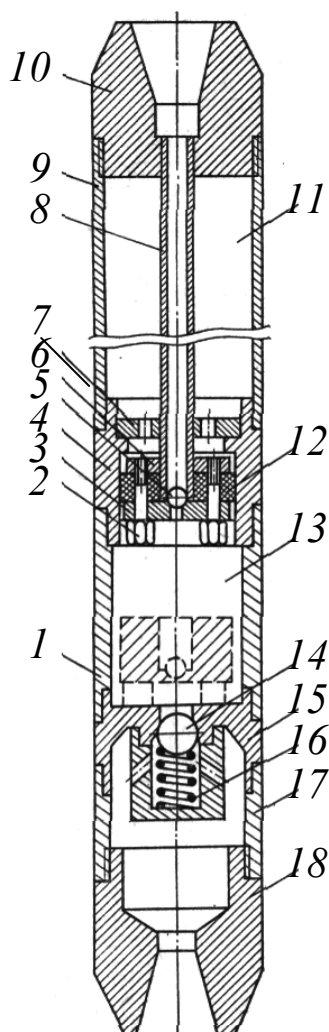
Тампонажное устройство ТСТ-1ГВ: 1, 9 – корпуса смесительной камеры и устройства; 2 – болт; 3, 6 – шайба ниппеля и верхняя; 4, 17 – ниппели; 5 – шарик; 7 – дозатор; 8 – центральная труба; 10, 18 – переходники верхний и нижний; 11 – контейнер; 12 – уплотнительная манжета; 13 – смесительная камера; 14 – шарик; 15 – обойма обратного клапана; 16 – пружина
